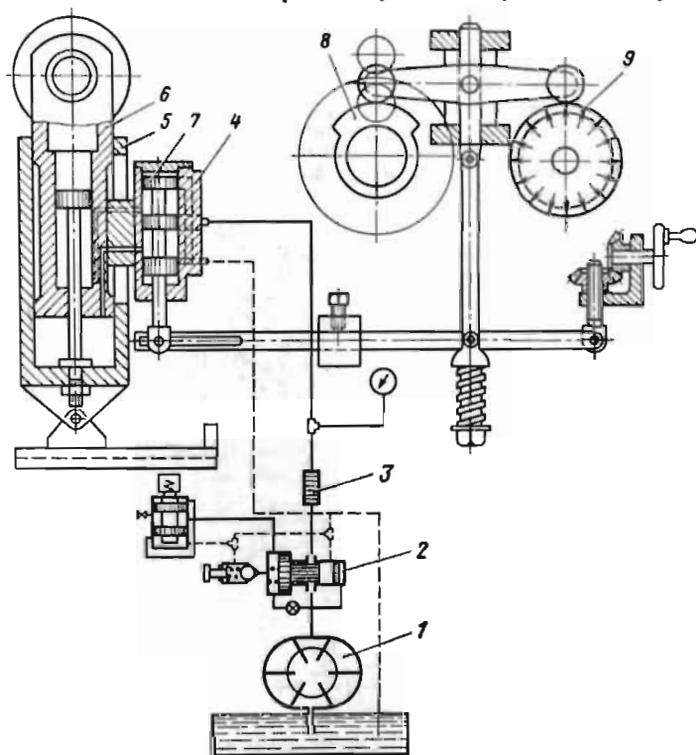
Гидравлический следящий привод станка ПГ-2М
